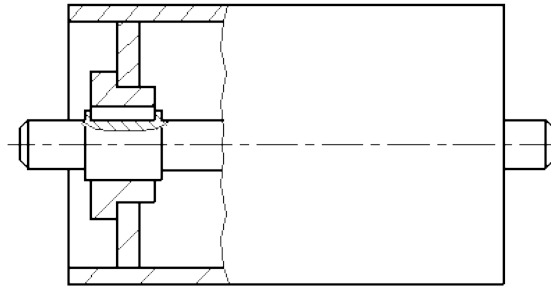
Пример изображения сварной сборочной единицы на сборочном чертеже изделия
